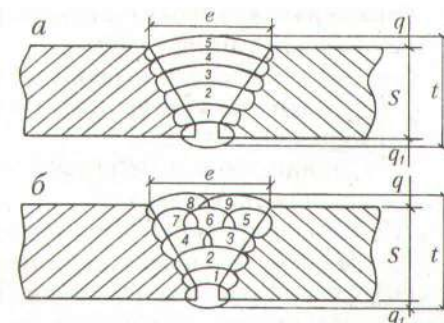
Зварювання багатшарових і багатпрохідних швів із зворотним підварюванням кореня:
